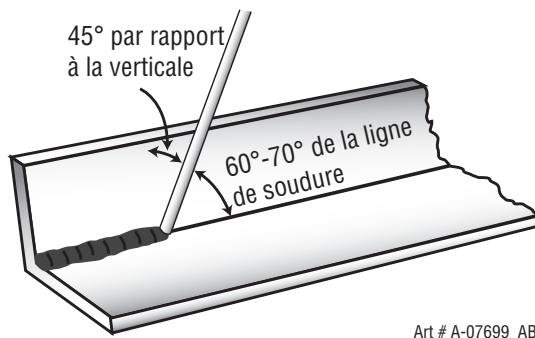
Position de l'électrode pour la soudure du joint HV
